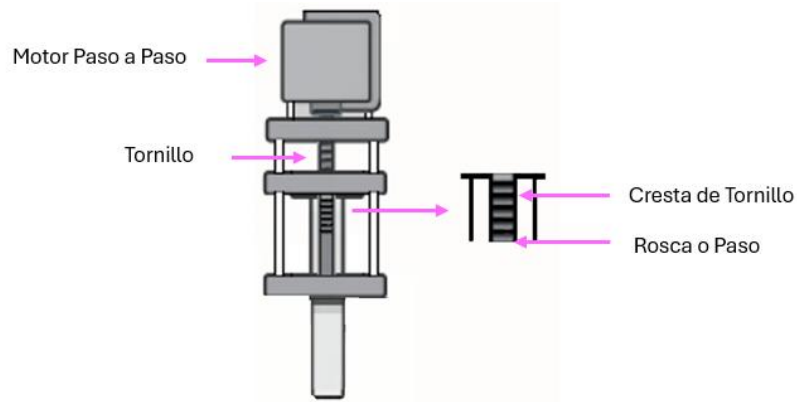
Esquema de la Impresora 3D Utilizada para la Fabricación de las Columnas y Prensa.
